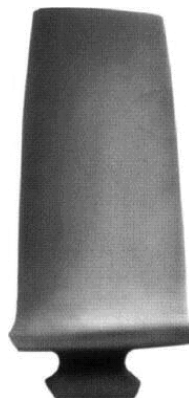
Лопатка ротора компрессора с нанесенным покрытием из нитрида титана [8]
